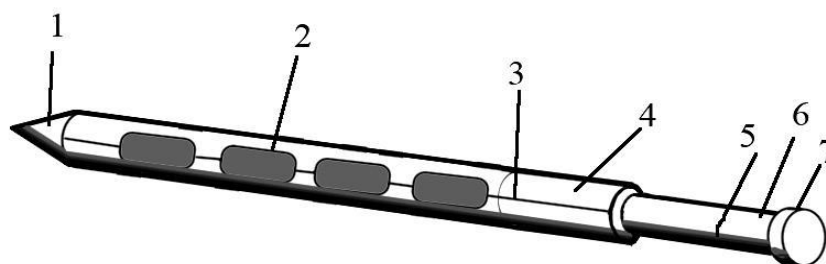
Щуп для бутылей: 1 - конус; 2 - окно; 3 - риска; 4 - наружный цилиндр; 5 - деление; 6 - внутренний цилиндр; 7 – ручка
